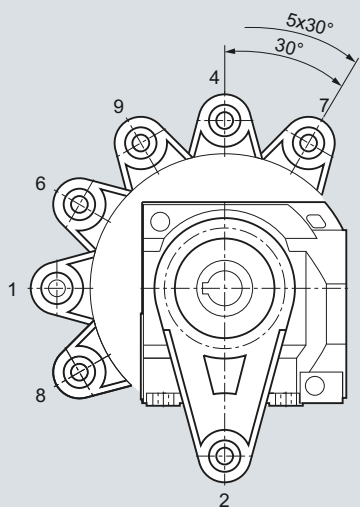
Kegelradgetriebe B in Aufsteckausführung
